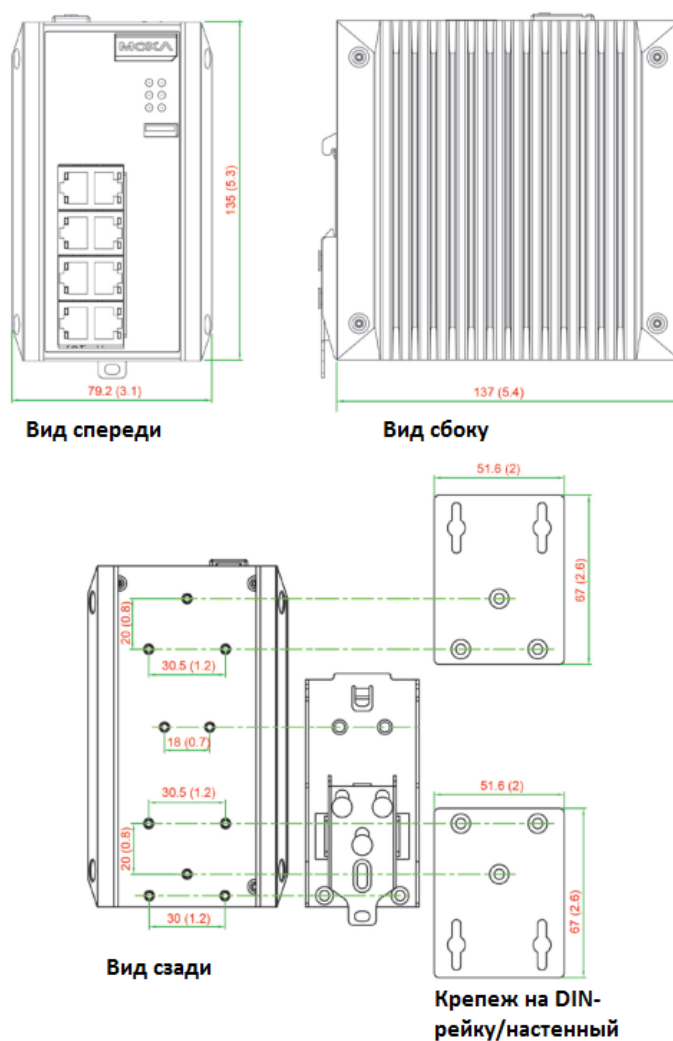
Установочные размеры коммутатора EDS-G508E
